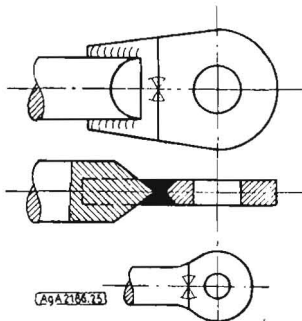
Gestaltung eines einfachen Gelenkauges, sie ist der Gestaltung nach Bild 23 fast gleichwertig, doch müssen die Schweißnähte, besonders die Stirnkehlnähte sehr sorgfältig ausgeführt werden. Es kann auch das Stabende breitgeschmiedet und das Gelenkauge stumpf angeschweißt werden. Hierbei ist aber darauf zu achten, daß durch das Ausschmieden keine Querschnittsverminderung eintritt
